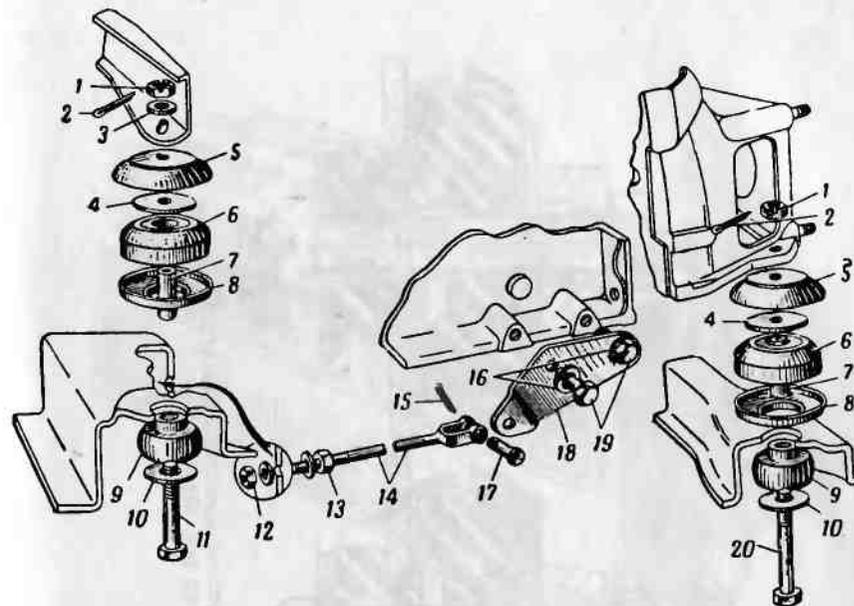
Детали крепления двигателя к поперечинам основания корпуса:
